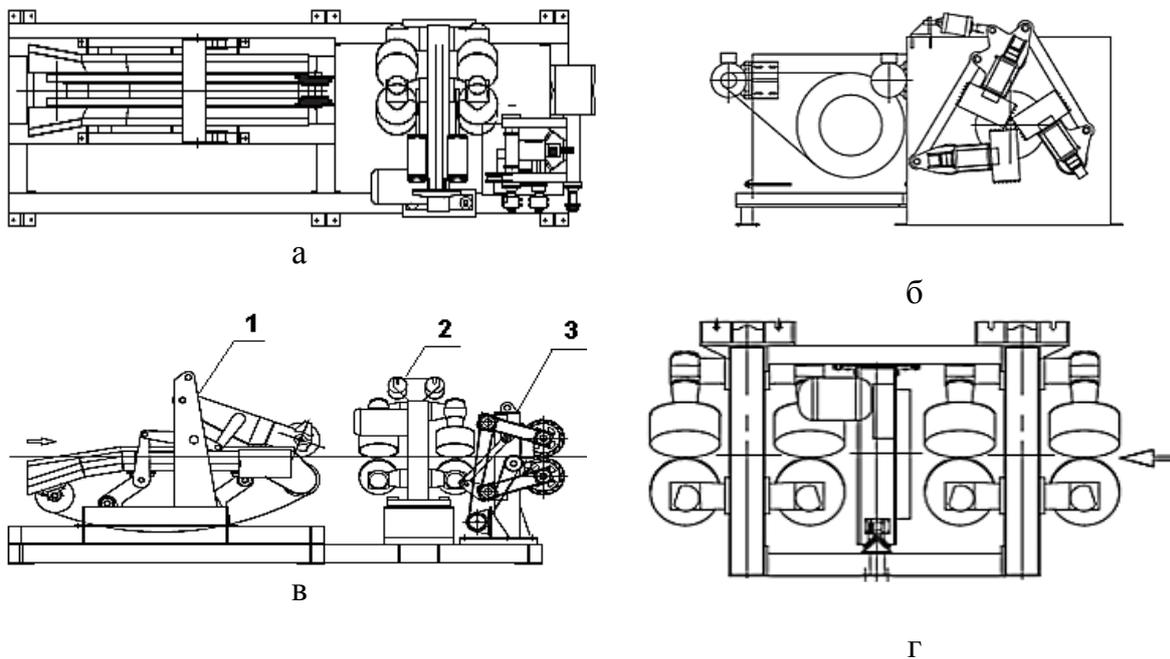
Схема станка Cambio: а – вид сверху; б – вид со стороны подачи (ротор выдвинут); в – вид сбоку; г – в двухроторной комплектации; 1– подающий конвейер; 2 – ротор с механизмом подачи; 3 – приемный механизм
